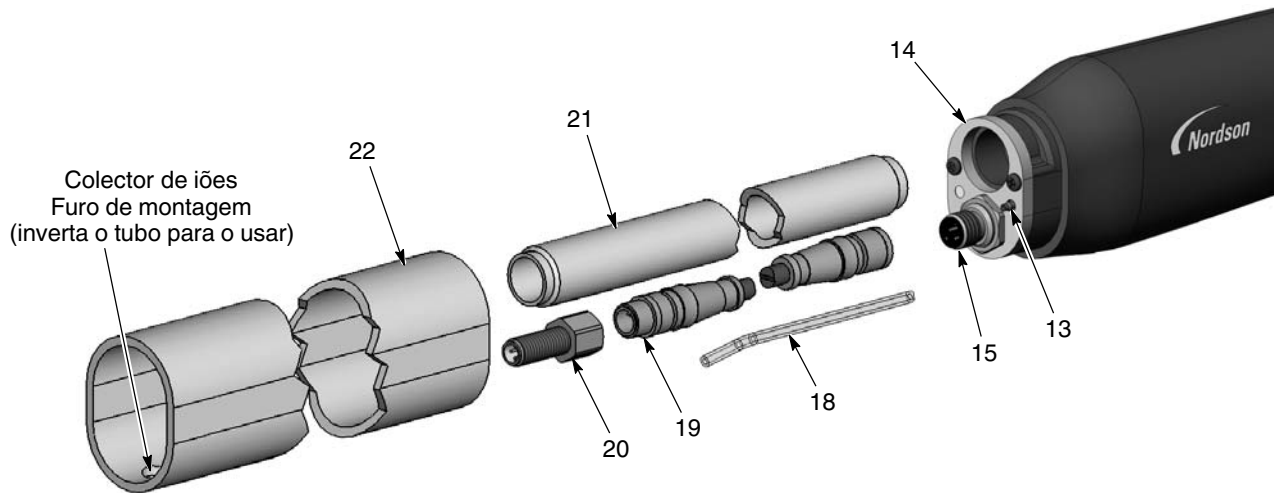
Desmontagem de pistola com tubo de suporte 2 de 5
